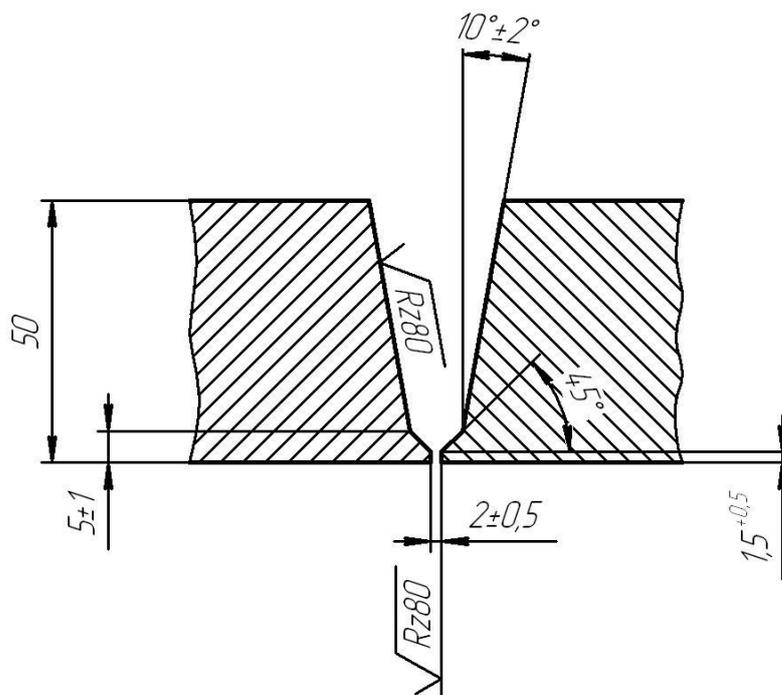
Подготовка кромок под сварку соединения Тр-6 [24]
